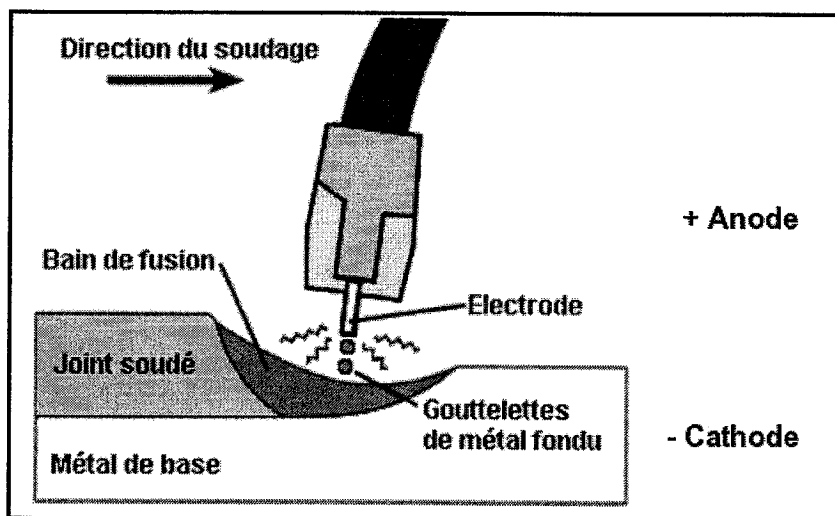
Représentation schématique du procédé de soudage GMAW
